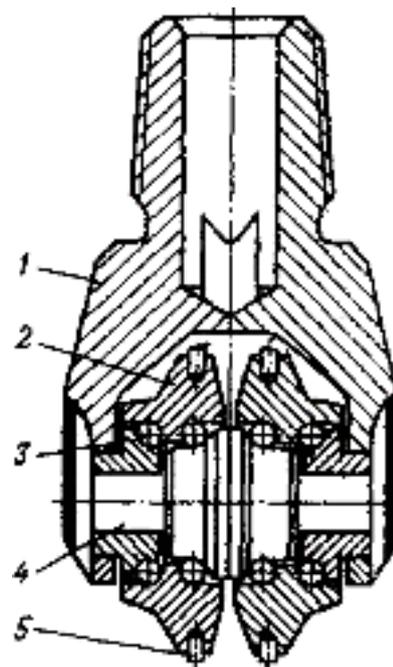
Дисковое долото: 1 – корпус; 2 – диск; 3 – подшипник; 4 – палец; 5 – твердосплавные зубки
